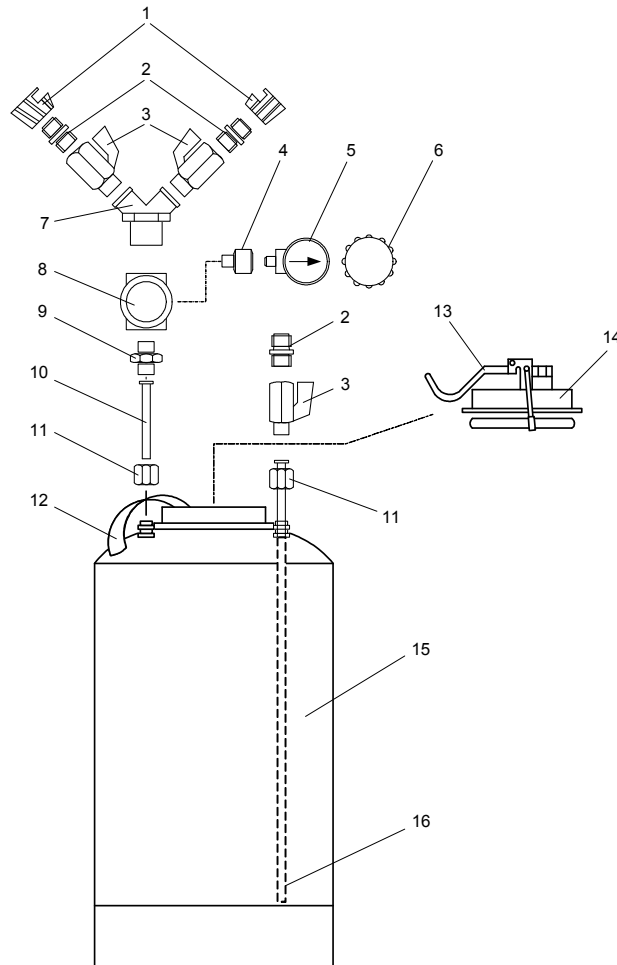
Конструкція ресиверного блоку: 1 – фіксатор шланга; 2 – перехідник; 3 – кран; 4 – перехідник манометра; 5 – манометр робочого тиску; 6 – захисний ковпак манометра; 7 – розгалужувач; 8 – регулювальний клапан; 9 – контргайка; 10 – трубка; 11 – гайка; 12 – ручка; 13 – фіксує ручка кришки бака; 14 – герметизуюча кришка; 15 – корпус бака; 16 – всмоктувальна трубка
